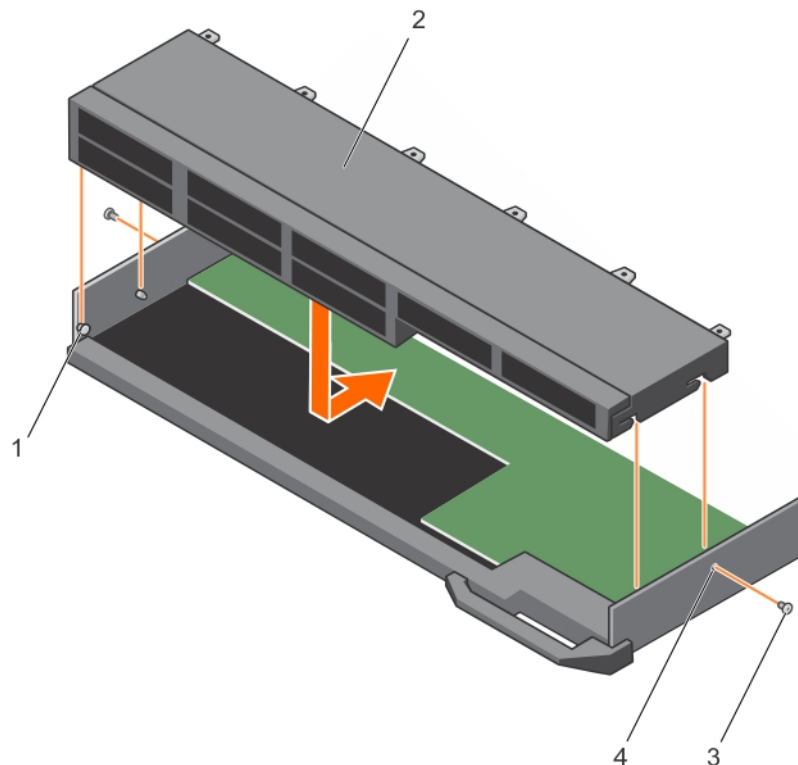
Installieren des Festplatten- bzw. SSD-Gehäuses
